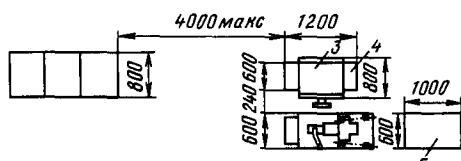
Общий вид и габариты индукционной закалочной установки ИЗ1-160/4:
